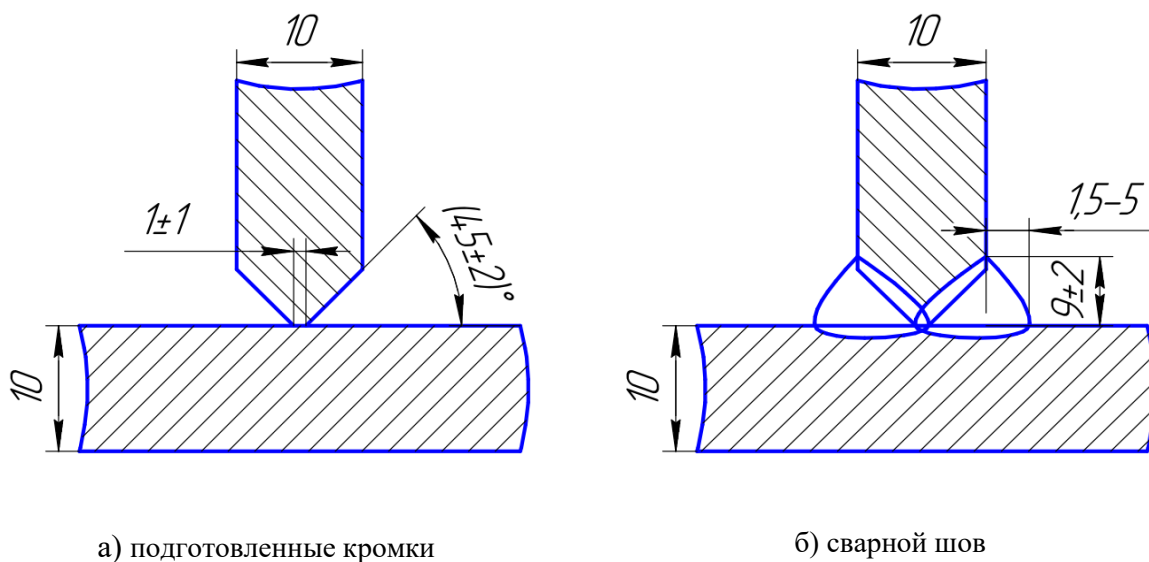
Форма подготовленных кромок и сварного шва
